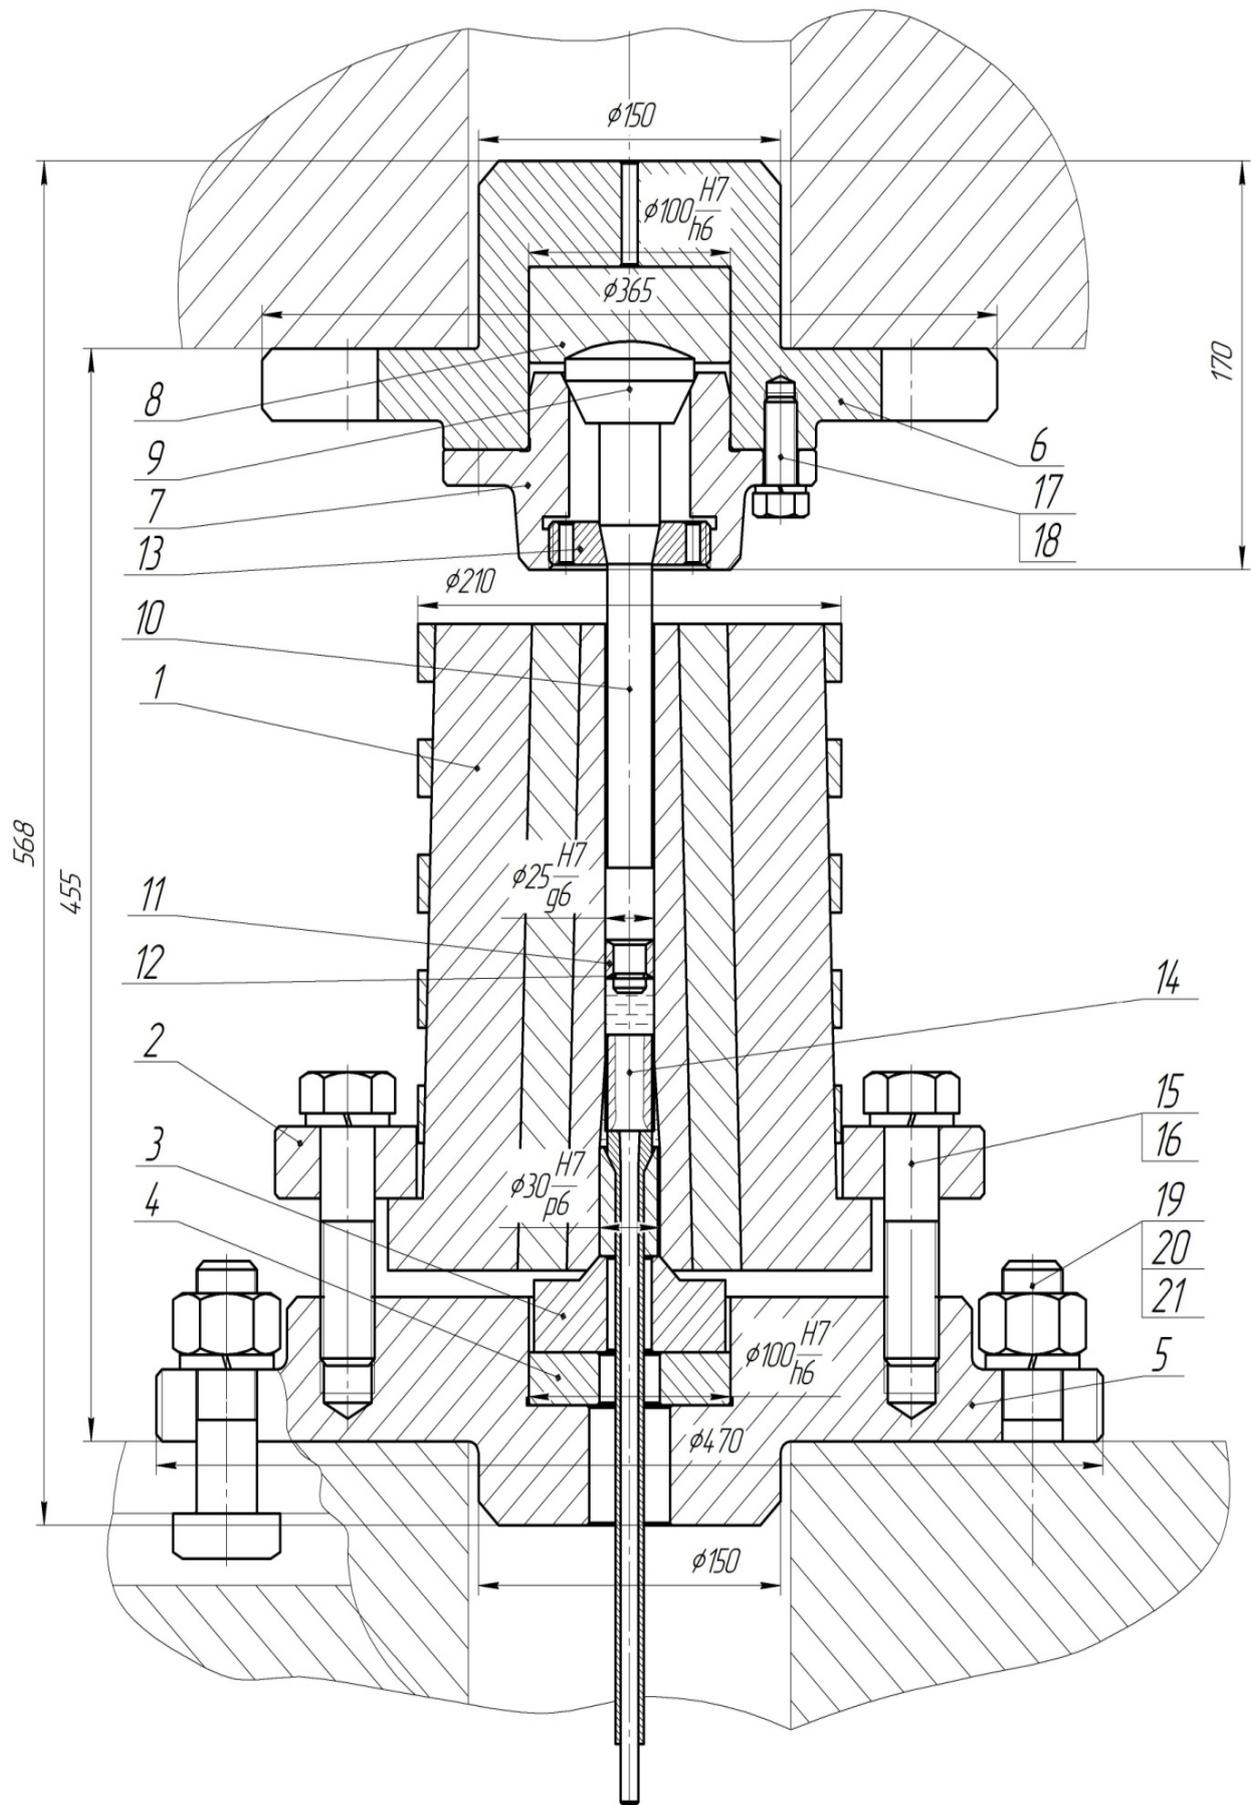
Конструкция штампа для гидроэкструзии с подвижной оправкой
